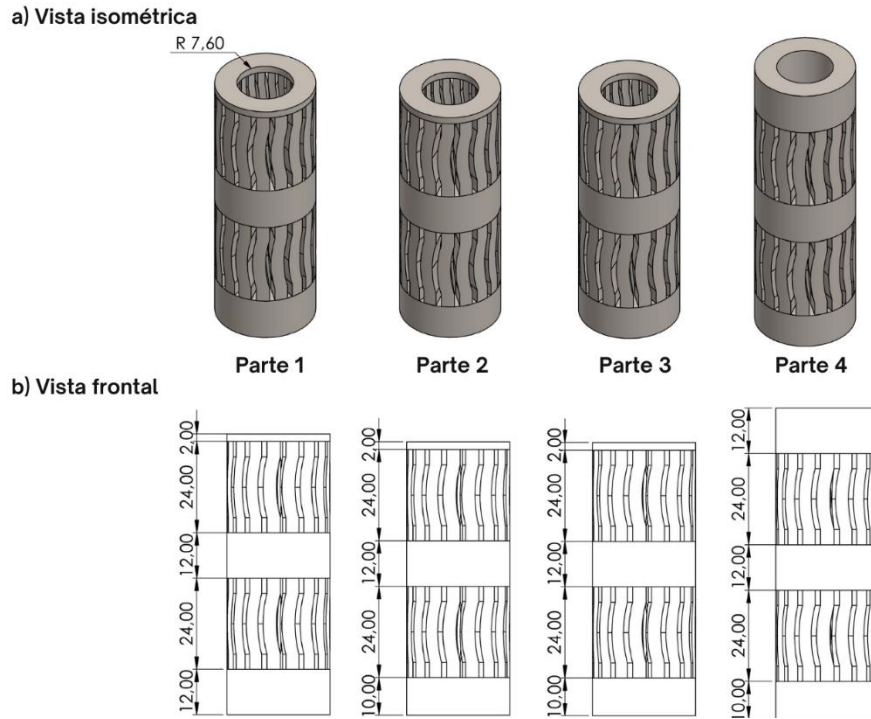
Divisão do CMM para impressão. Em a) Vista isométrica. Em b) Vista frontal
